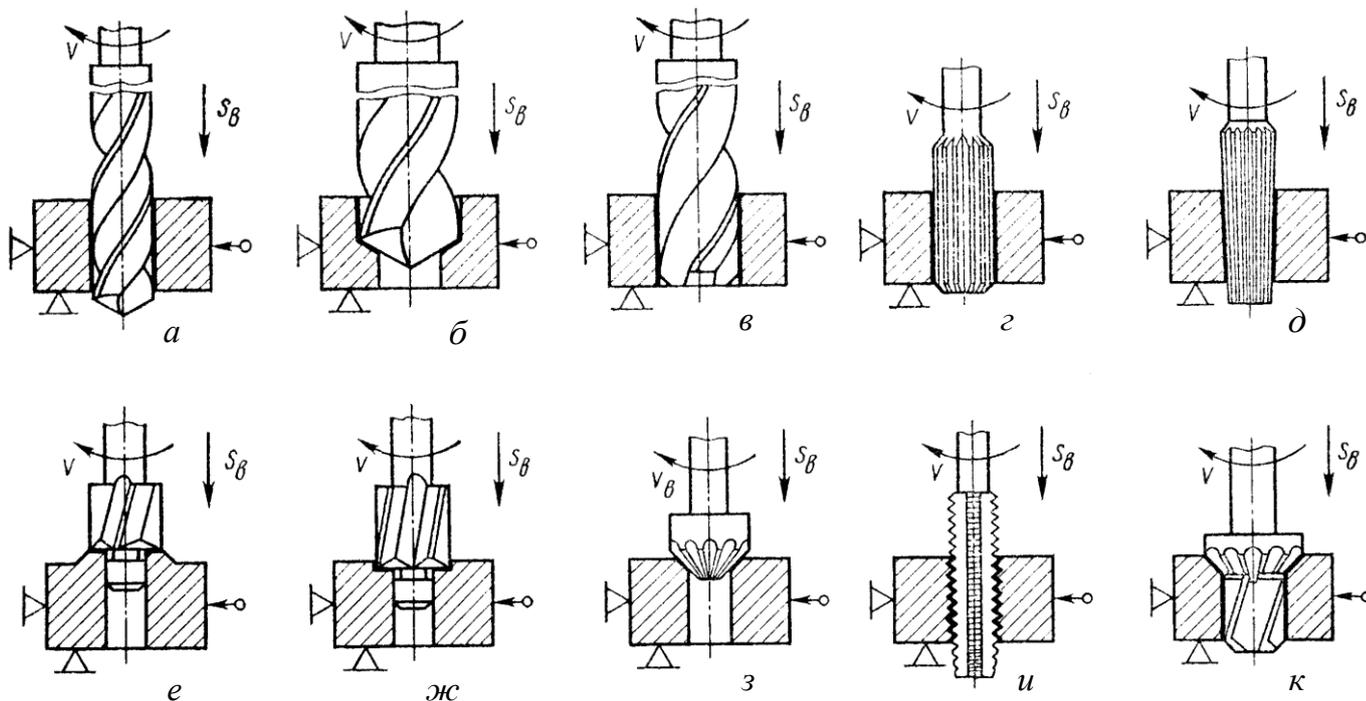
Основные схемы обработки заготовок на сверлильных станках:
